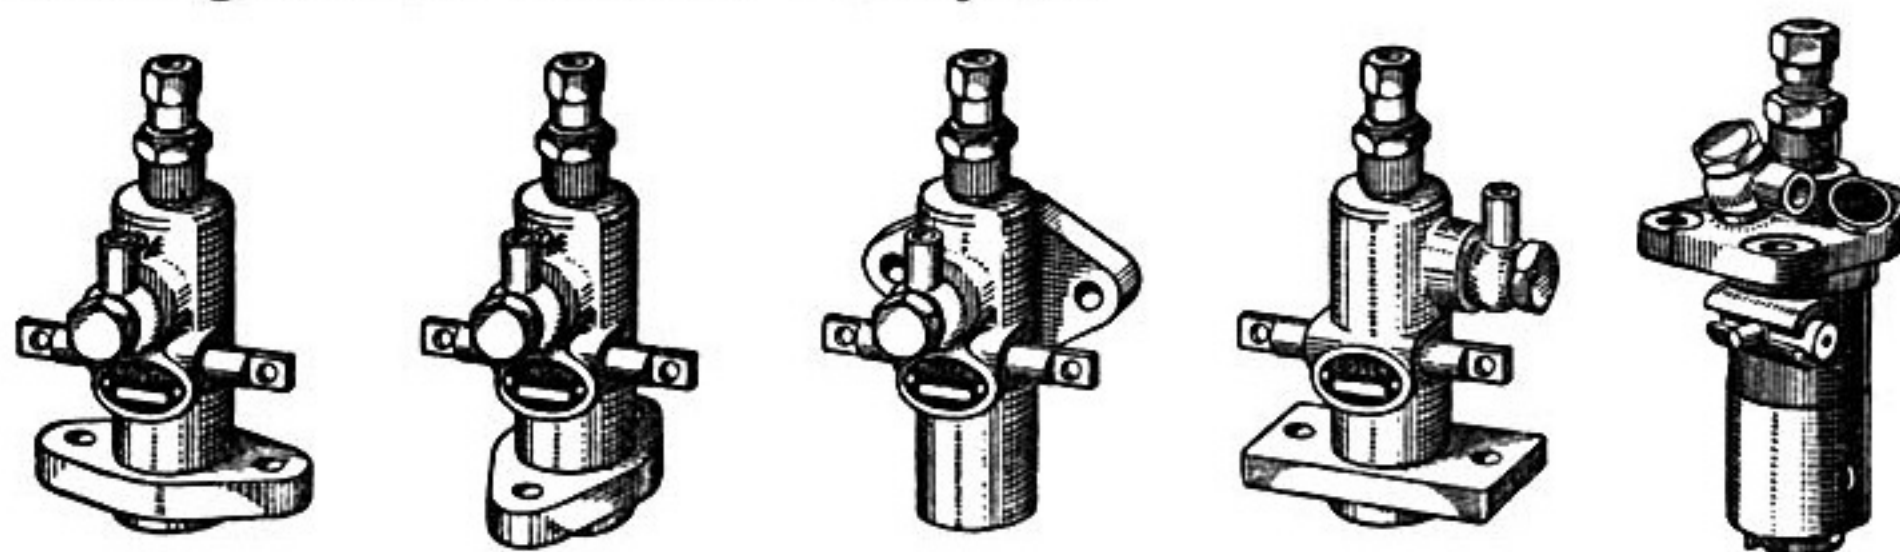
PF-Einzylinderpumpen mit verschiedenen Flanschlagen
